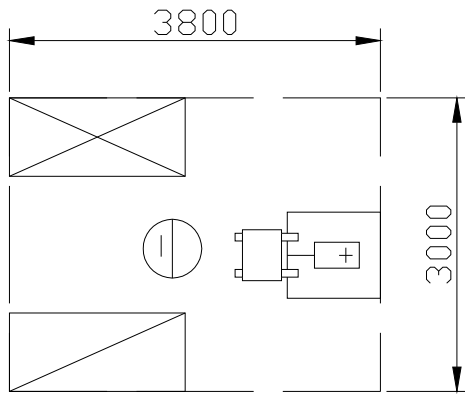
Схема организации рабочего места у сверлильно-пазовального станка СВПА-2 $F = 11,4 \text{ м}^2$
